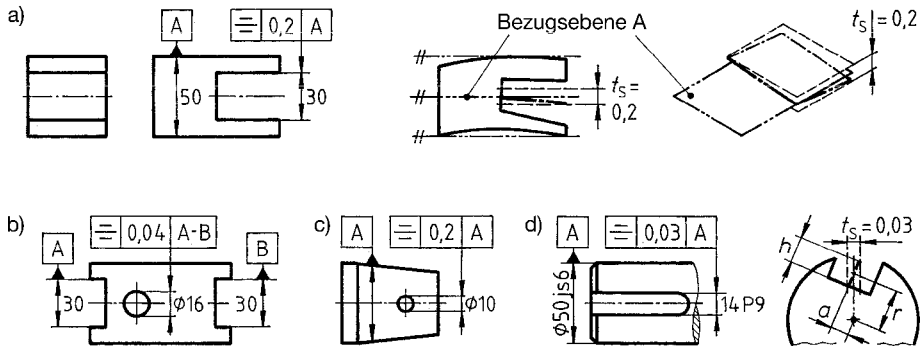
Symmetrietolerierung. a) Tolerierung einer Nut, mit Bezugsermittlung und Toleranzzone; b) Bohrung in einem Baukastenelement; c) Querloch in einem Kegel; d) Tolerierung einer Passfedernut, mit Toleranzzone und Grenzlage
